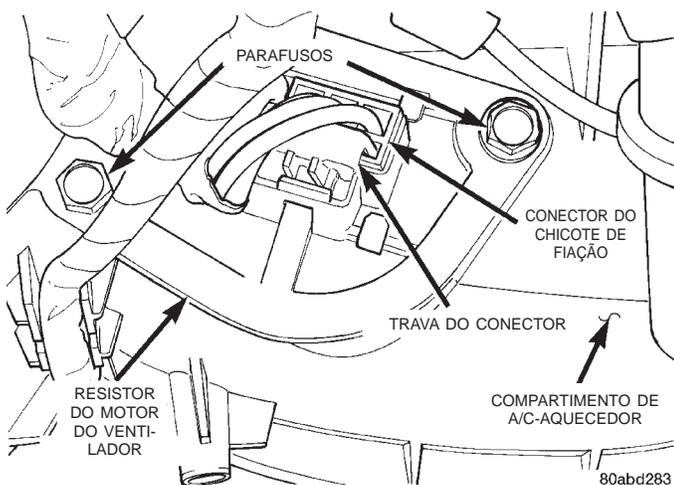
Remoção/Instalação do Resistor do Motor do Ventilador
